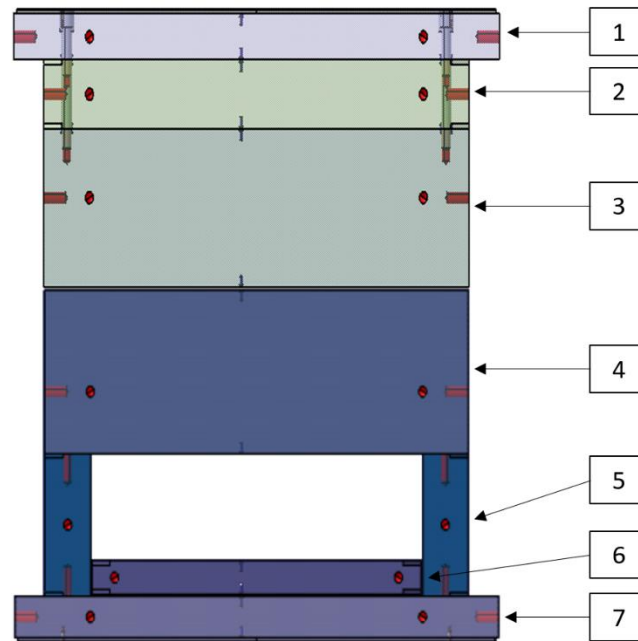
Representa o da numera o das placas de um molde de duas placas.
